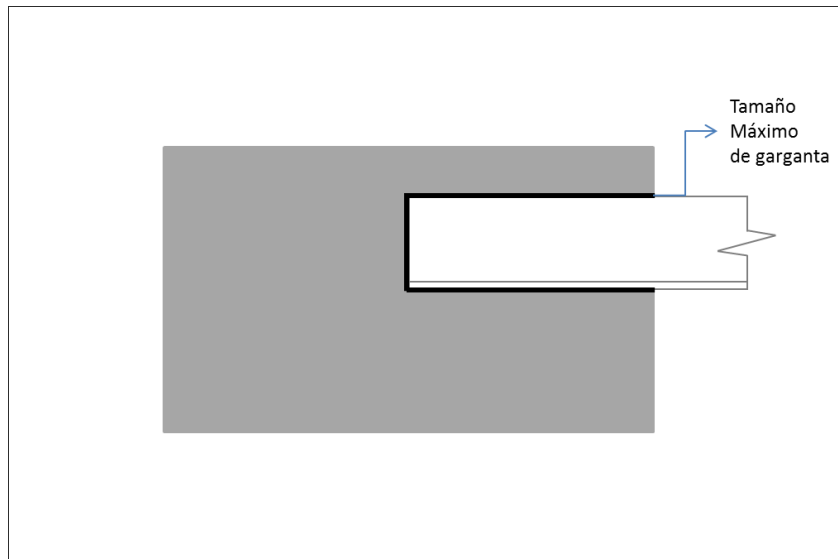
Patrón de soldadura utilizado en el caso 2.
